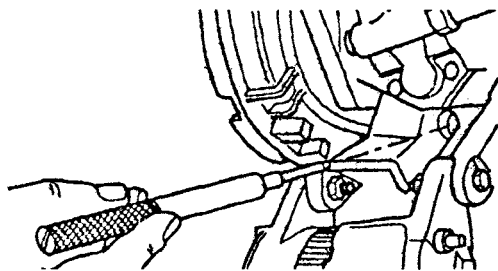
Место размещения оправки для установки коленчатого вала в положение ВМТ 1-го цилиндра
